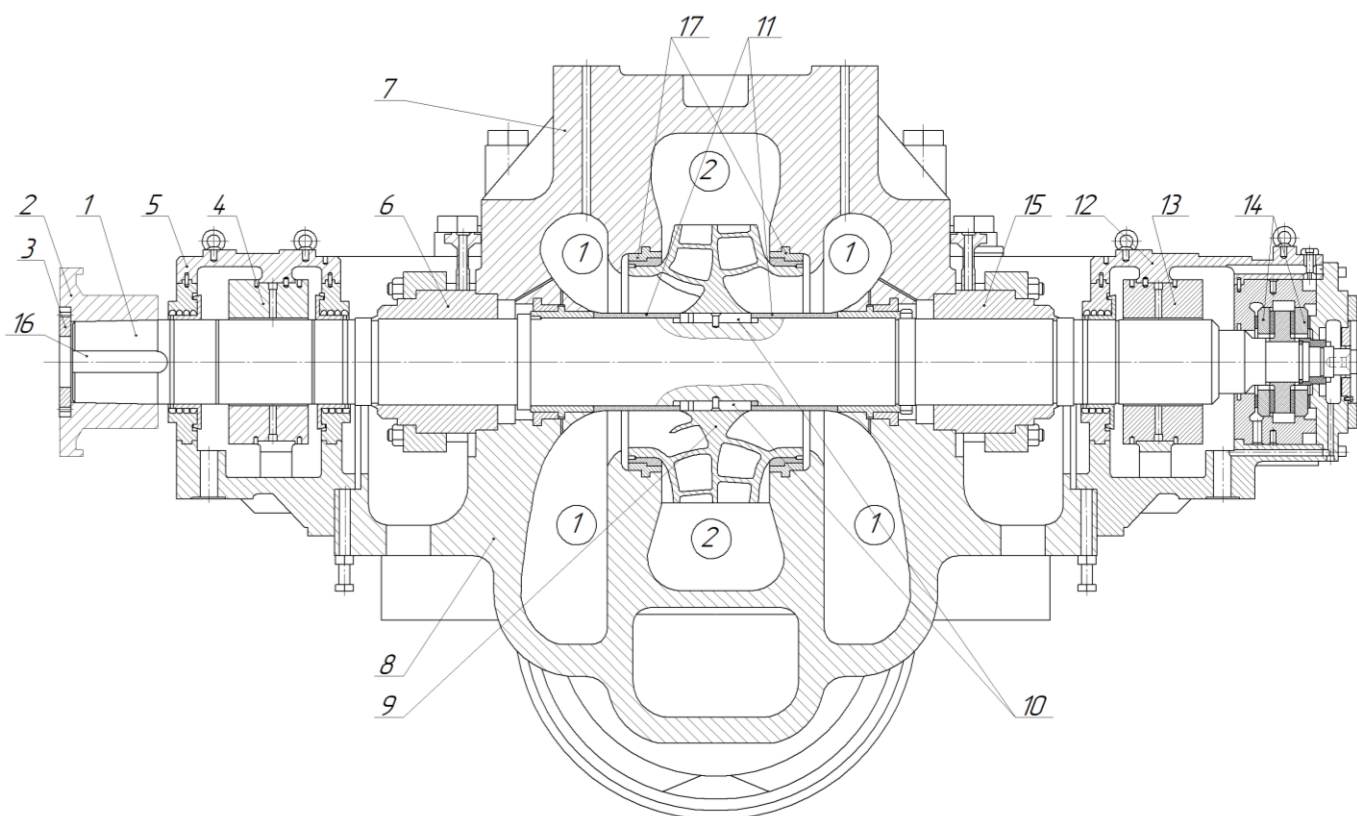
Сборочный чертеж насоса НМ-10000-380
